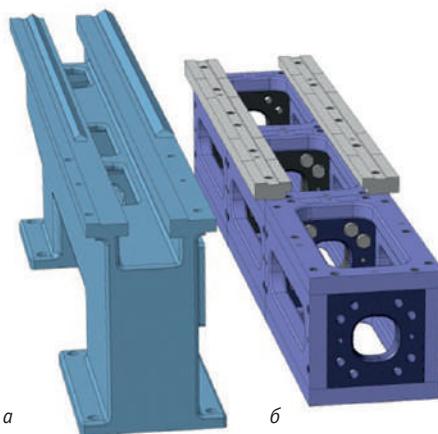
Пример сложной отливки: *а* – литая станина токарного станка; *б* – модульная конструкция станины токарного станка
